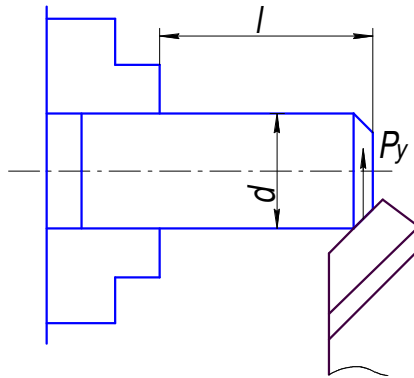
Схема для расчета подачи, допускаемой прочностью заготовки, установленной в патроне
